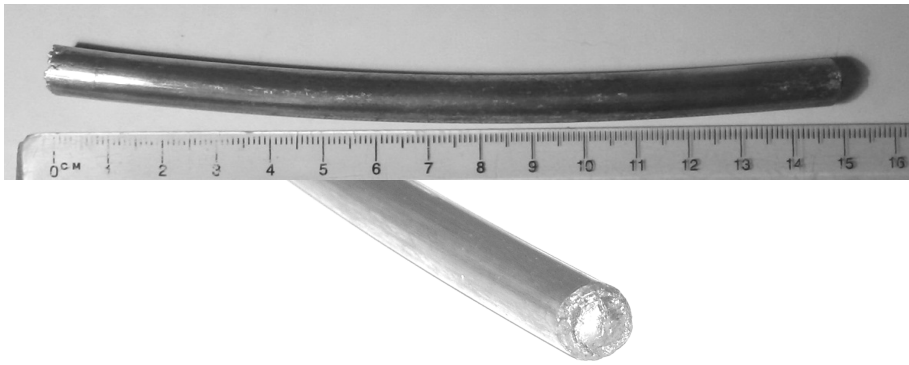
Пруток, видавлений із пресовки з компенсатором
